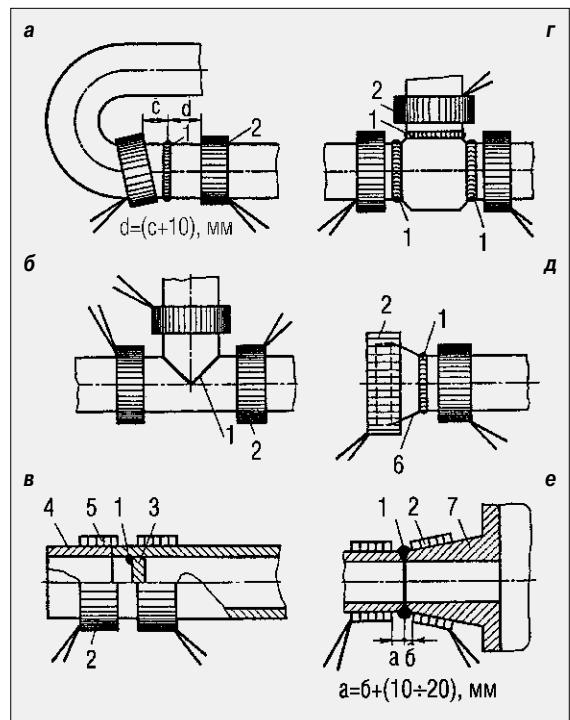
Рекомендуемые схемы установки ГЭН для термообработки сварных соединений повышенной трудности:
